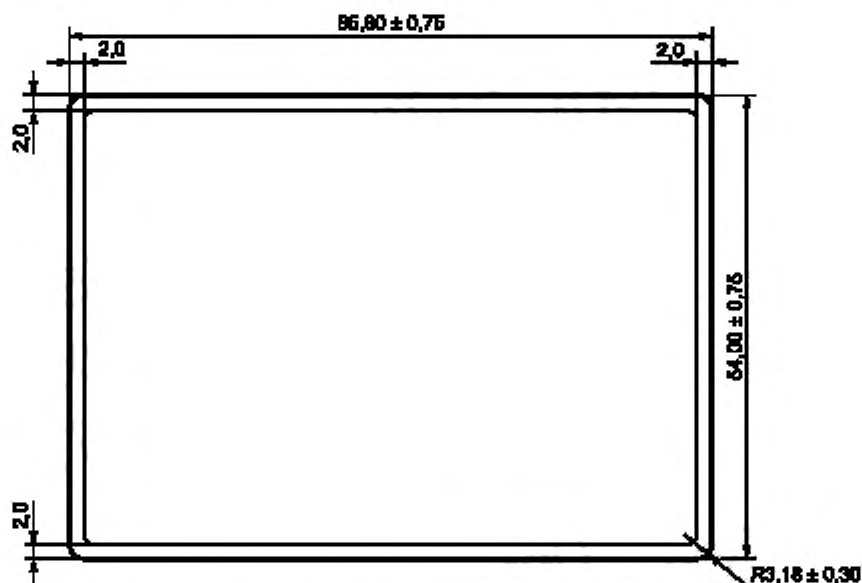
Размеры и допуски документа ПД-1
